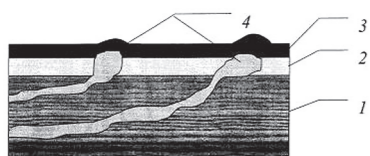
Общепринятая схема покрытия: 1 – древесина; 2 – грунт и (или) шпатлевка; 3 – покрывной слой ЗДП; 4 – смола (смоляные ходы)
